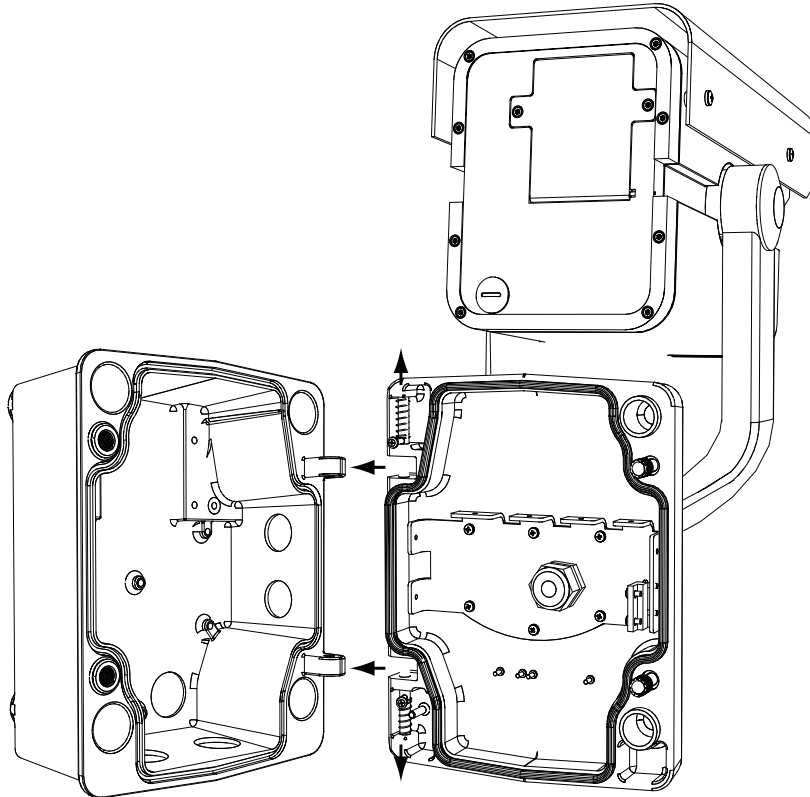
Ausrichten des Kastenscharniers für die Kamera
